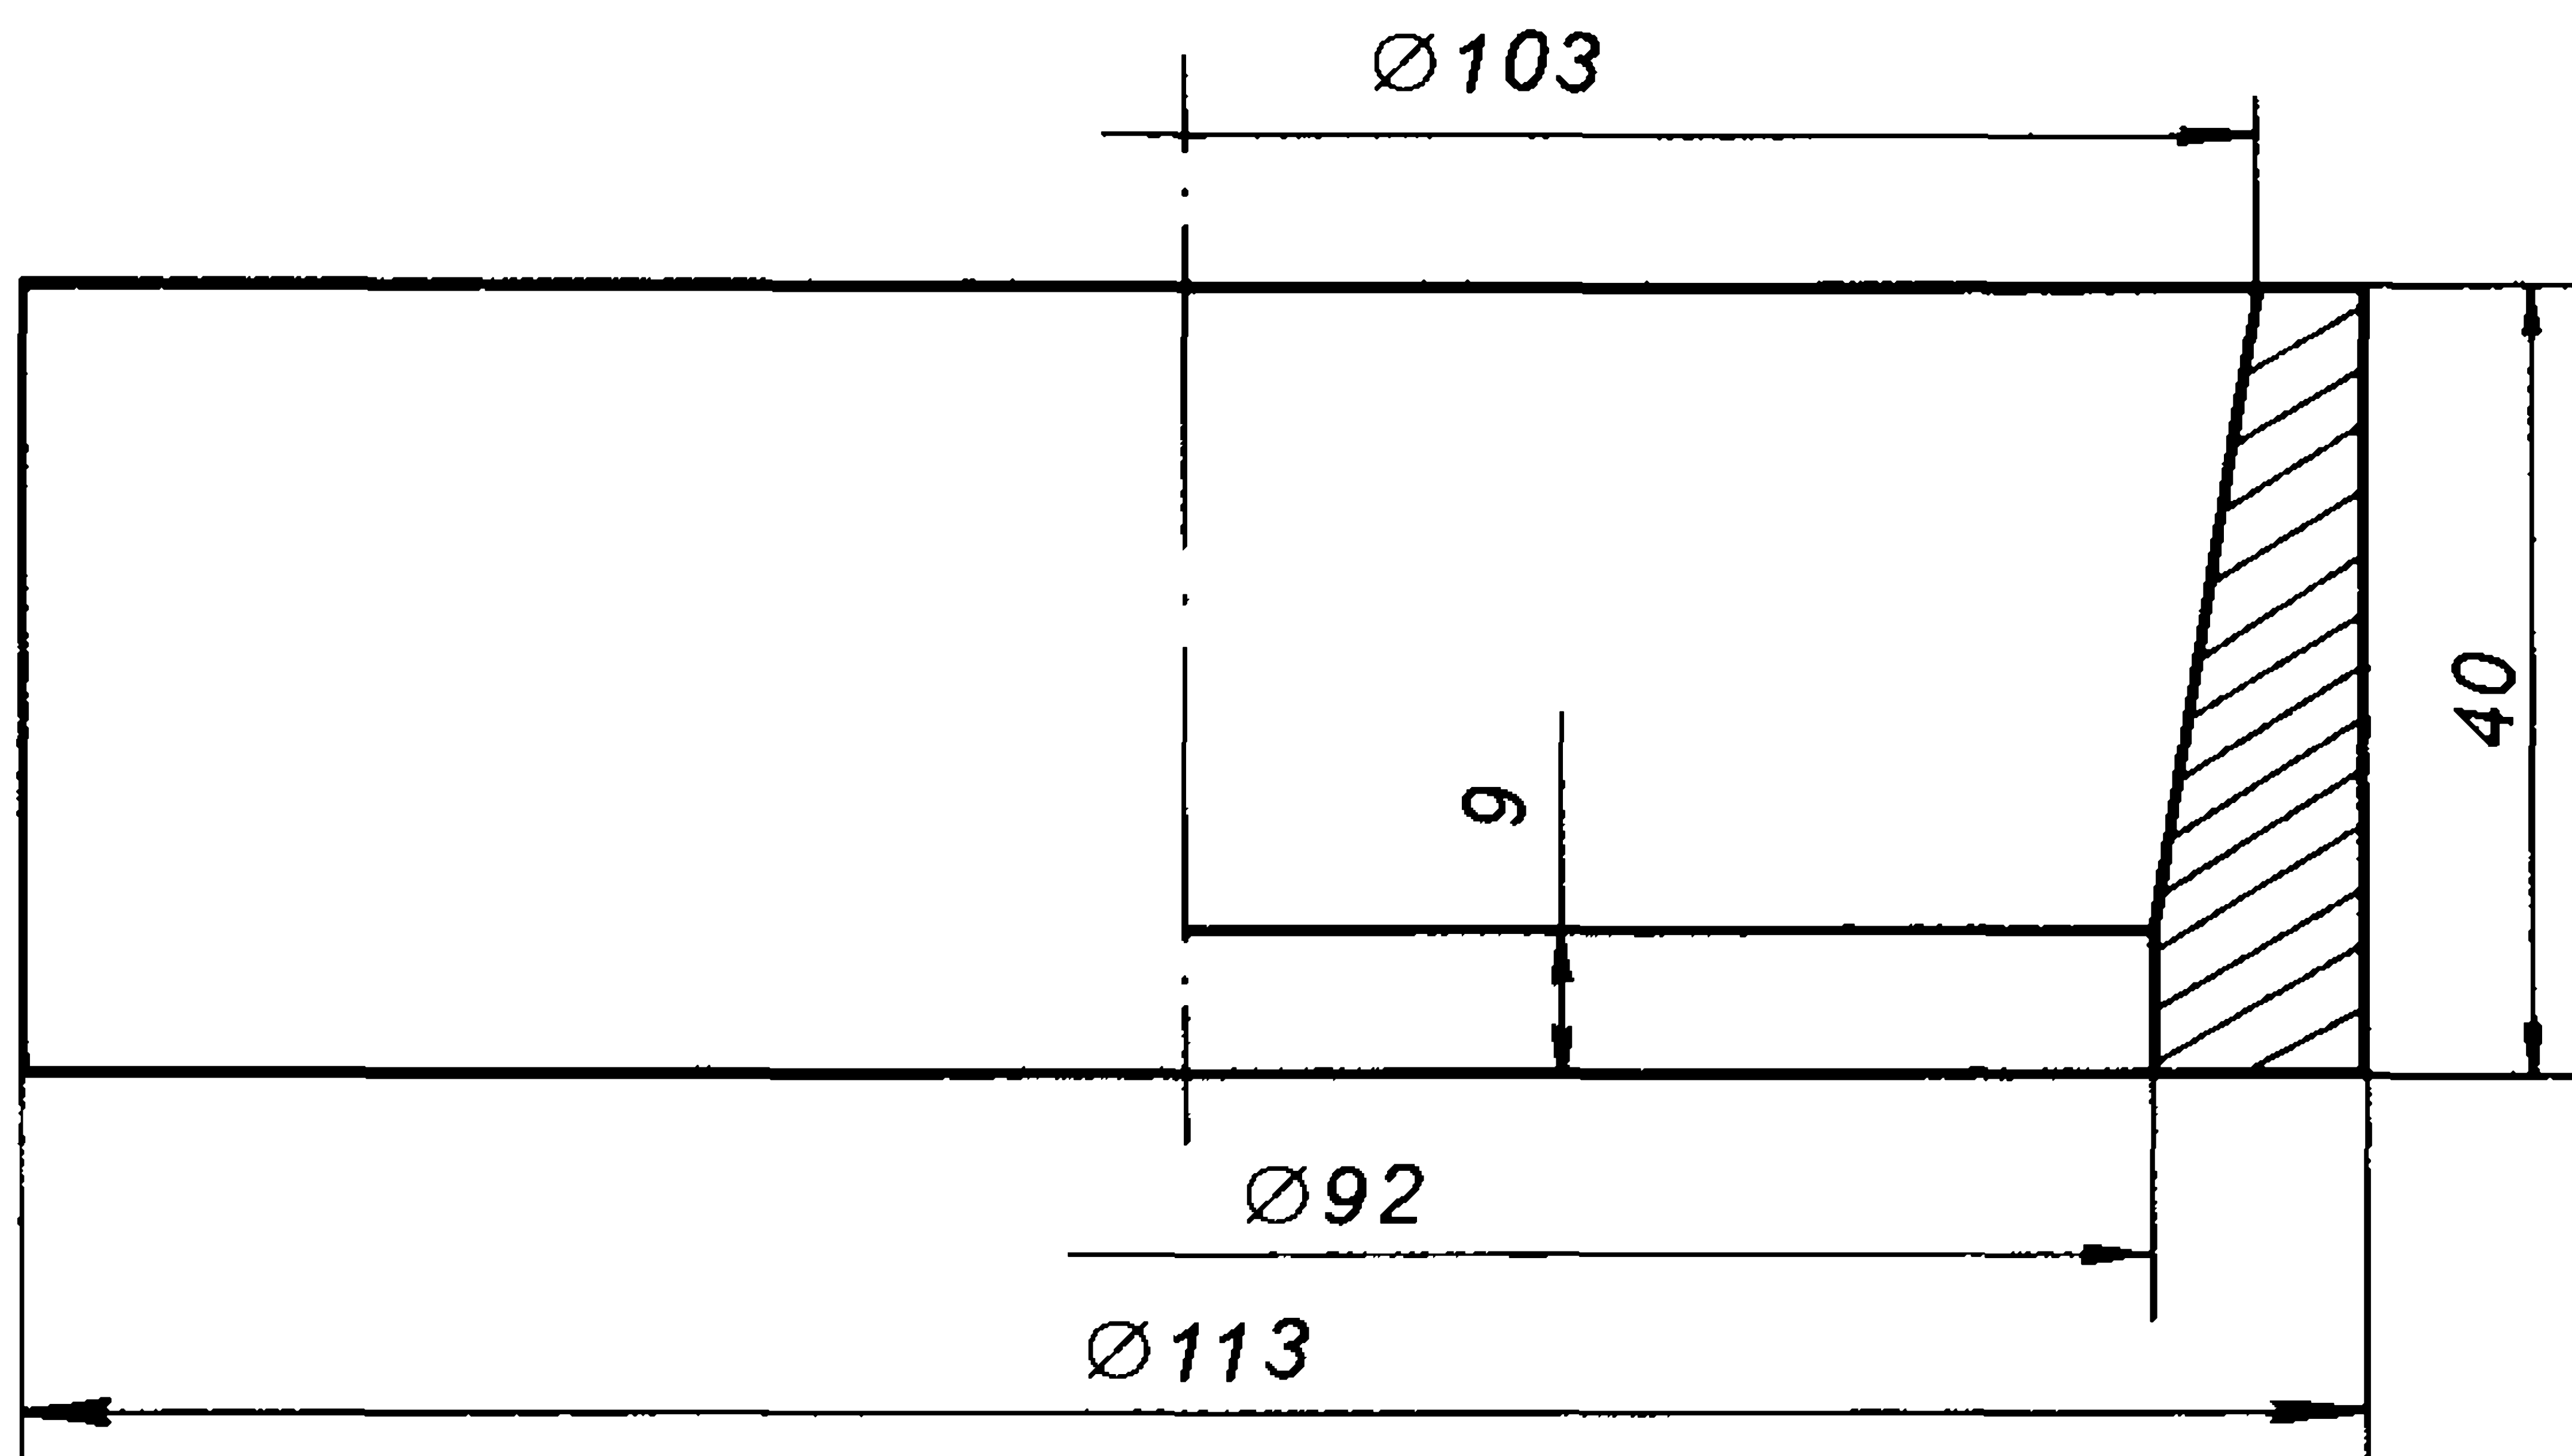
Установка поршня с кольцами в гильзу с помощью оправки
